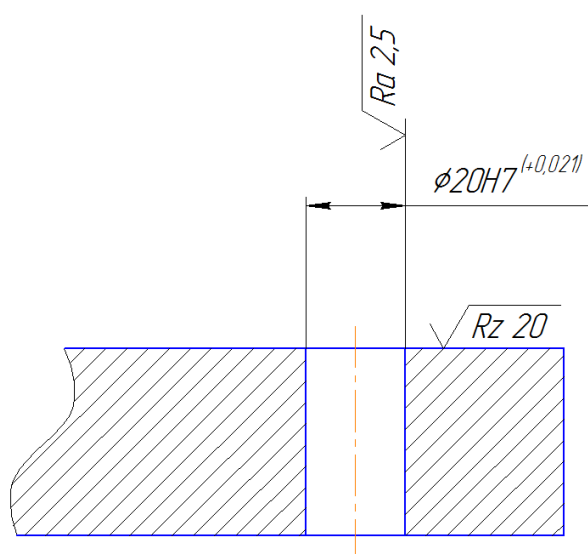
Шероховатость поверхности и допуск на размер
